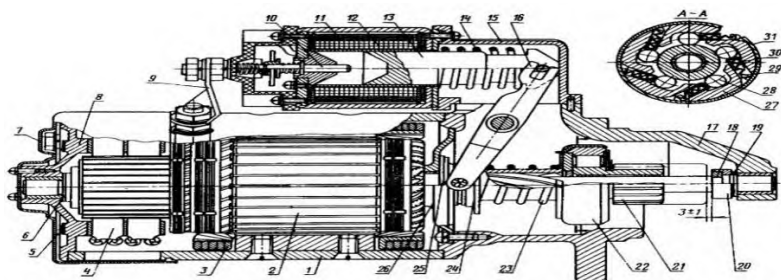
Стартер СТ-212-А: 1 — корпус; 2 — якорь; 3 — катушка возбуждения; 4 — щетка; 5 — шпилька; 6 — шайба; 7 — кожух; 8 — крышка; 9 — соединительная шина; 10 — плунжер; 11 — втягивающая обмотка реле; 12 — удерживающая обмотка реле; 13 — якорь реле; 14 — возвратная пружина; 15 — фланец реле; 16 — рычаг; 17 — крышка; 18 — упорное полукольцо; 19 — шайба; 20 — обойма; 21 — шестерня привода; 22 — муфта свободного хода; 23 — буферная пружина; 24 — втулка отводки; 25 — шайба; 26 — промежуточная опора; 27 — наружная обойма; 28 — ролик; 29 — пружина; 30 — плунжер; 31 — крышка муфты.
